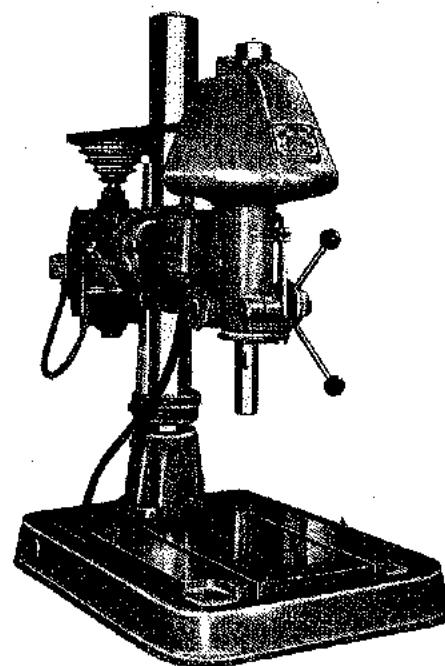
Taladradora sensible sobre banco (Cincinnati Lathe & Tool Co.)
